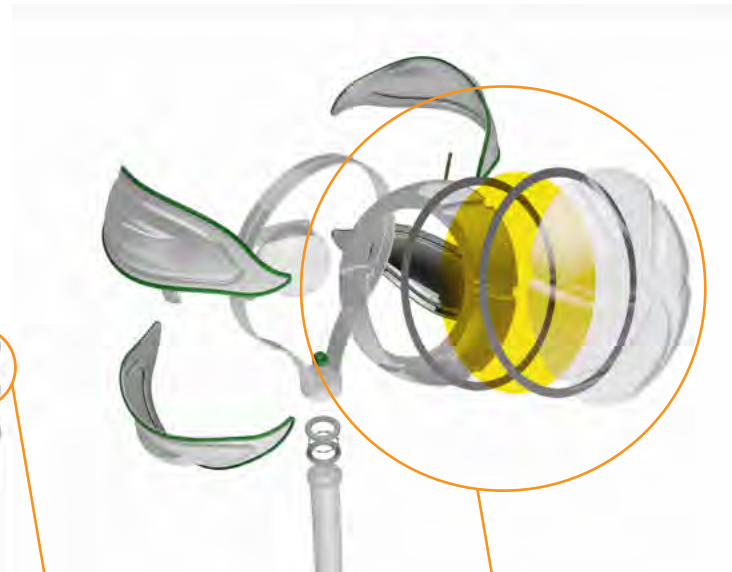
a 161. Detalle Propuesta final. Fuente: El autor.
